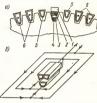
Индуктор для закалки боковых поверхностей и впадин двух зубьев шестерни большого модуля непрерывно-последовательным
